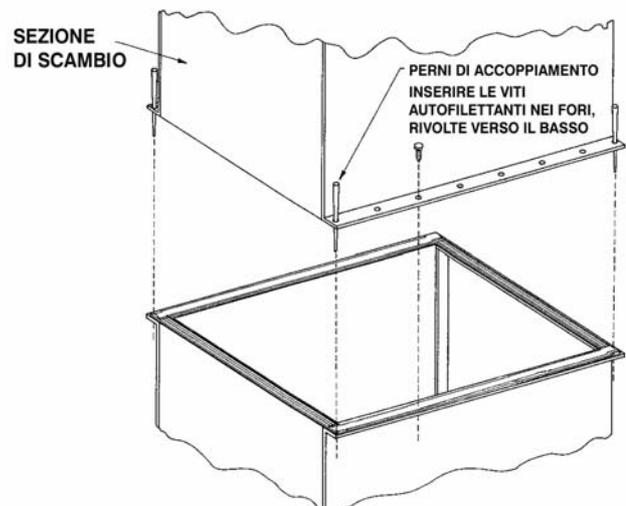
Assemblaggio della sezione superiore con la sezione inferiore.
